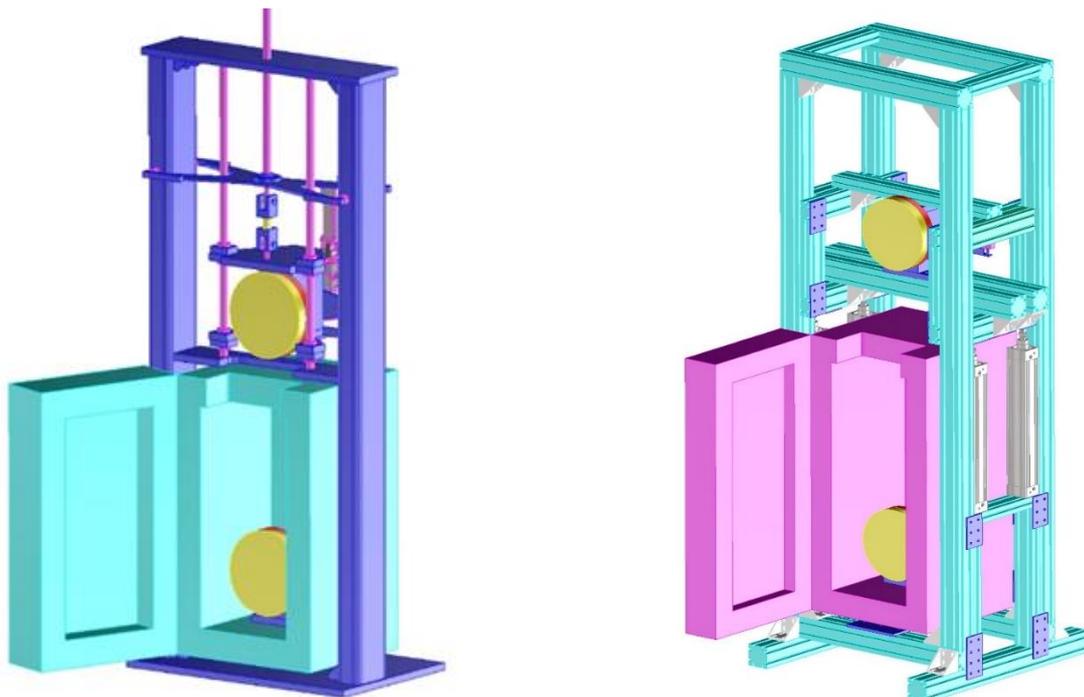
Gestellvarianten Stahl-Schweißbaugruppe (links) und verschraubte Aluminiumprofile (rechts)
